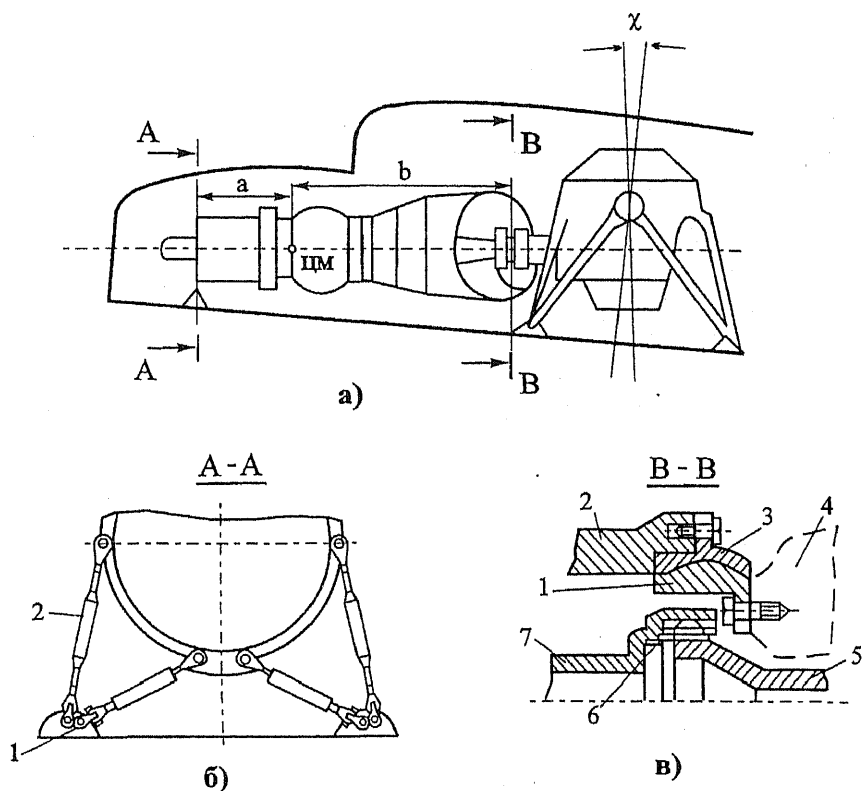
Схема крепления двигателя со сферической опорой:
